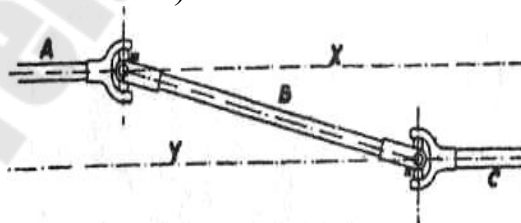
Карданный вал: А — ведущий вал мотора; тип — карданные сочленения (шарниры); В — карданный вал; С — вал дифференциала
